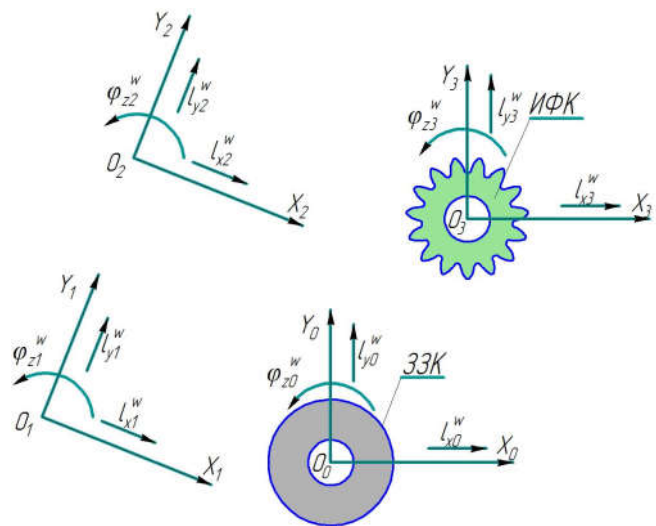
Обобщенная геометрико-кинематическая схема движения плоского исходного формообразующего зубчатого контура (ИФК) относительно заготовки зубчатого контура
